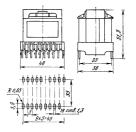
Общий вид, габаритные размеры и разметка печатнои платы для установки импульсных трансформаторов питания
